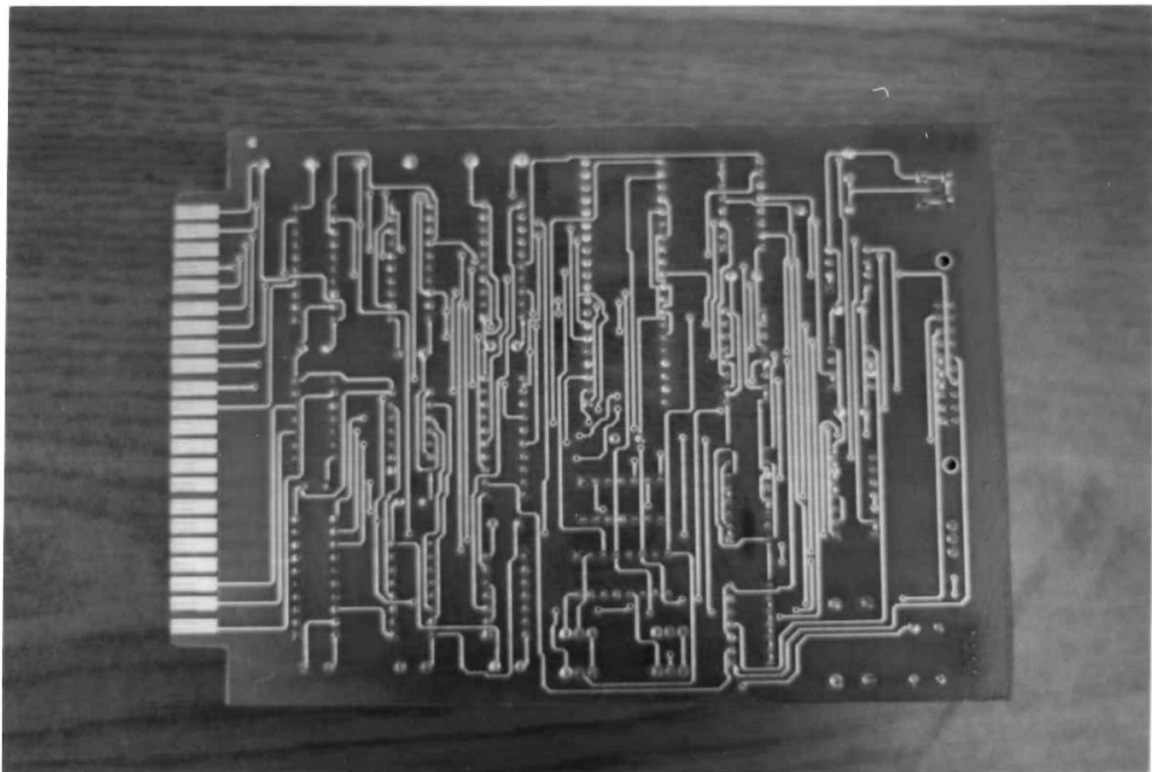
Fotografía de la tarjeta por el lado de soldadura.
